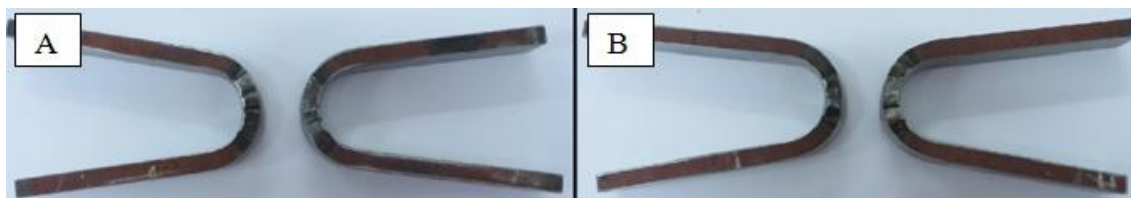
Ensaio de dobragem - Provetes soldados com fio
